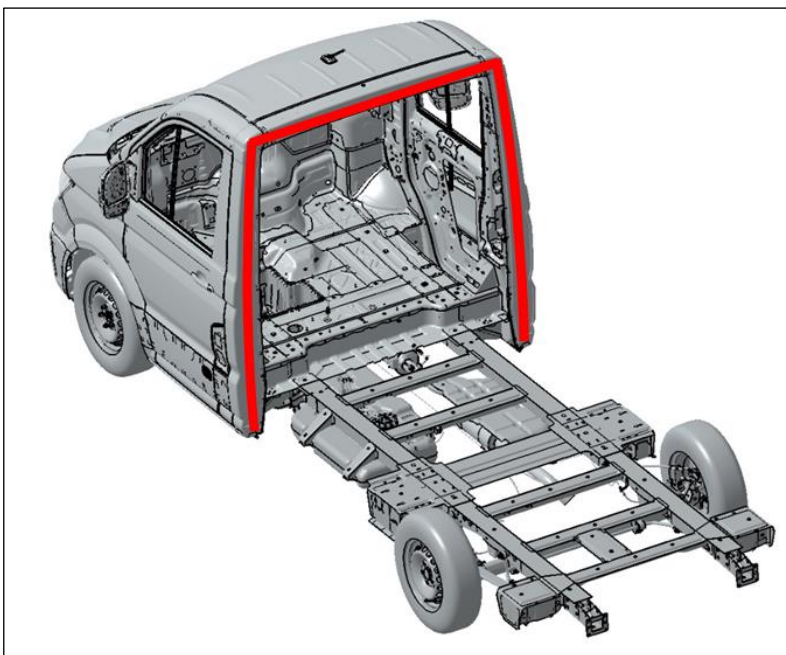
superfici di incollaggio del telaio piano del Crafter, collegamento della parete posteriore con la traversa del tetto e la cabina di guida, montante B
